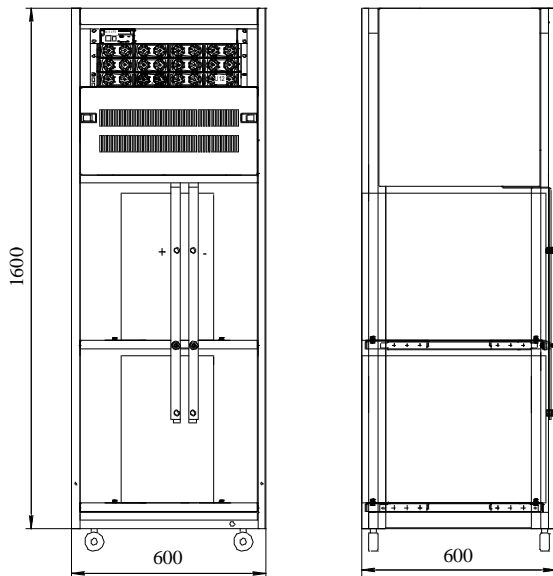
Габаритный чертеж УКРЗА-5 48(60)/400(360)-1212
